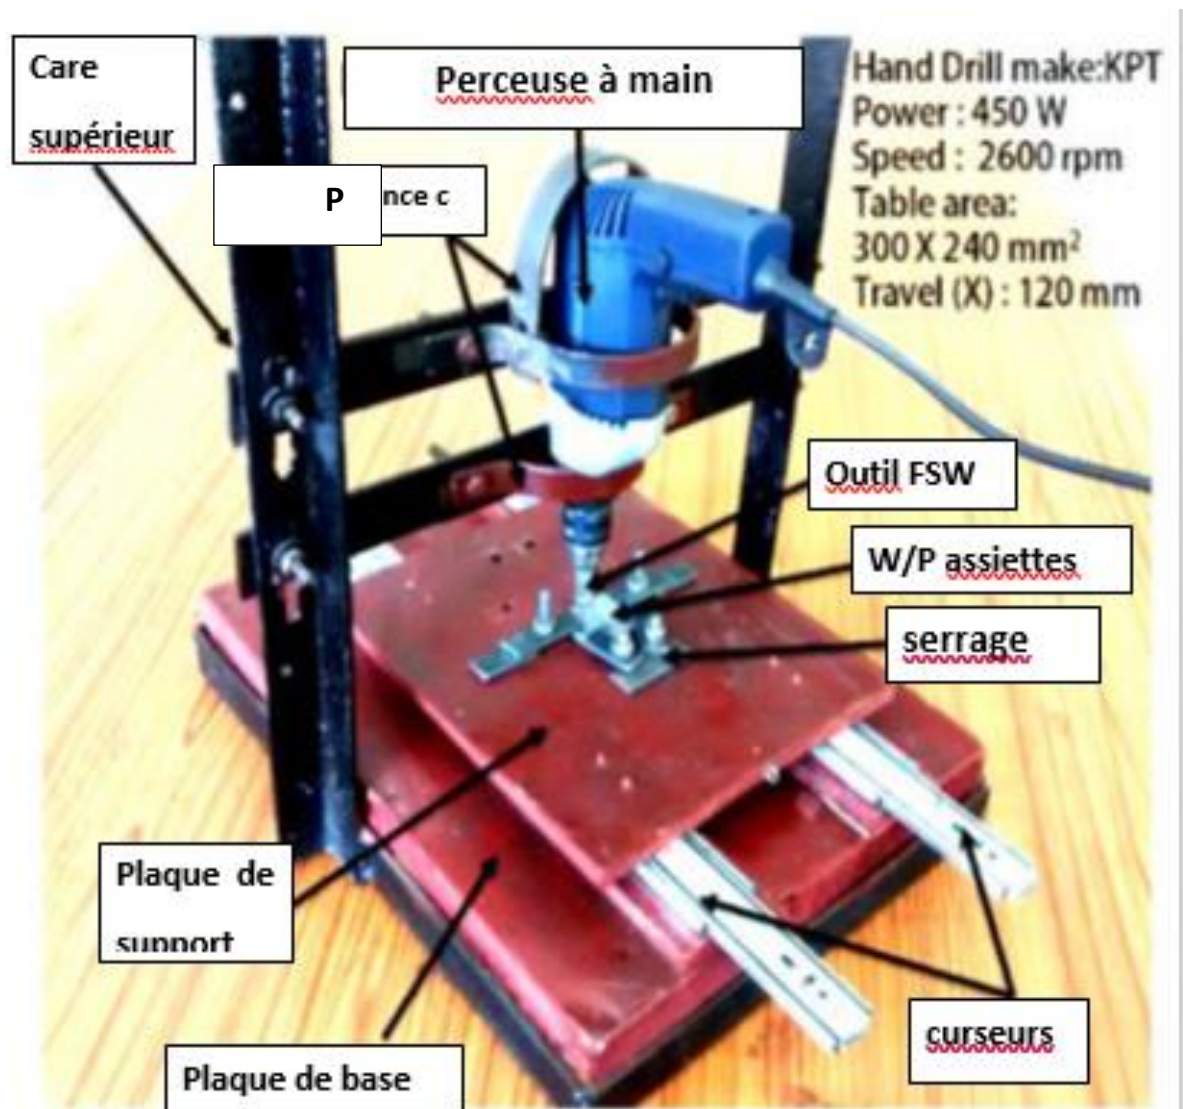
La machine de FSW modèle de MohdAneesSiddiqui et al [57].
